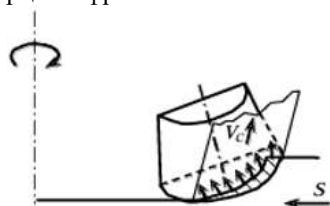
Напрямок сходу стружки при торцевому фрезеруванні ножами з конічною передньою та плоскою задньою поверхнями
